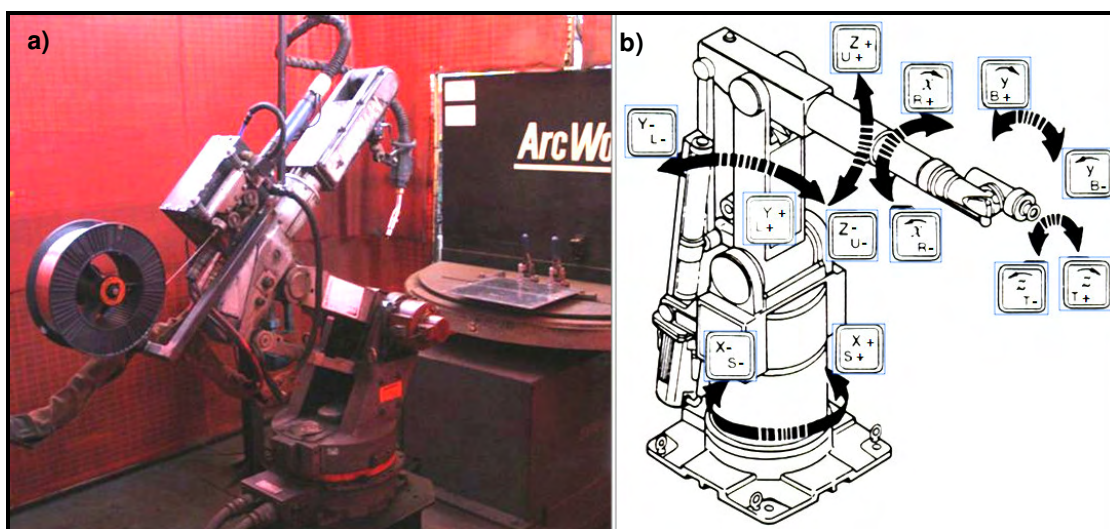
Robô de soldagem utilizado: (a) disposição dos equipamentos para a soldagem; e (b) ilustração dos graus de liberdade (Adaptado de MOTOMAN, 1995).
